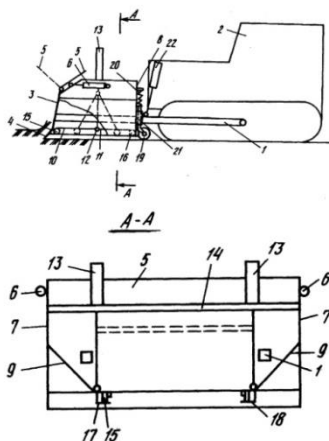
1- толкающие брусья, 2- ходовые тележки базовой машины, 3- отвал, 4- режущий нож, 5- подвижный козырёк, 6- гидроцилиндр, 7- боковая стенка, 8- задняя стенка, 9- днище ковша, 10 - 11-подвижные части днища ковша, 12 -соединительный шарнир, 13- дополнительный гидроцилиндр, 14- банка, 15-16- катки, 17-18- направляющие, 19- опорные колеса, 20- пружины, 21- корпус, 22- гидроцилиндры. Другие концы подвижных частей имеют опорные катки, перемещающиеся в направляющих.
